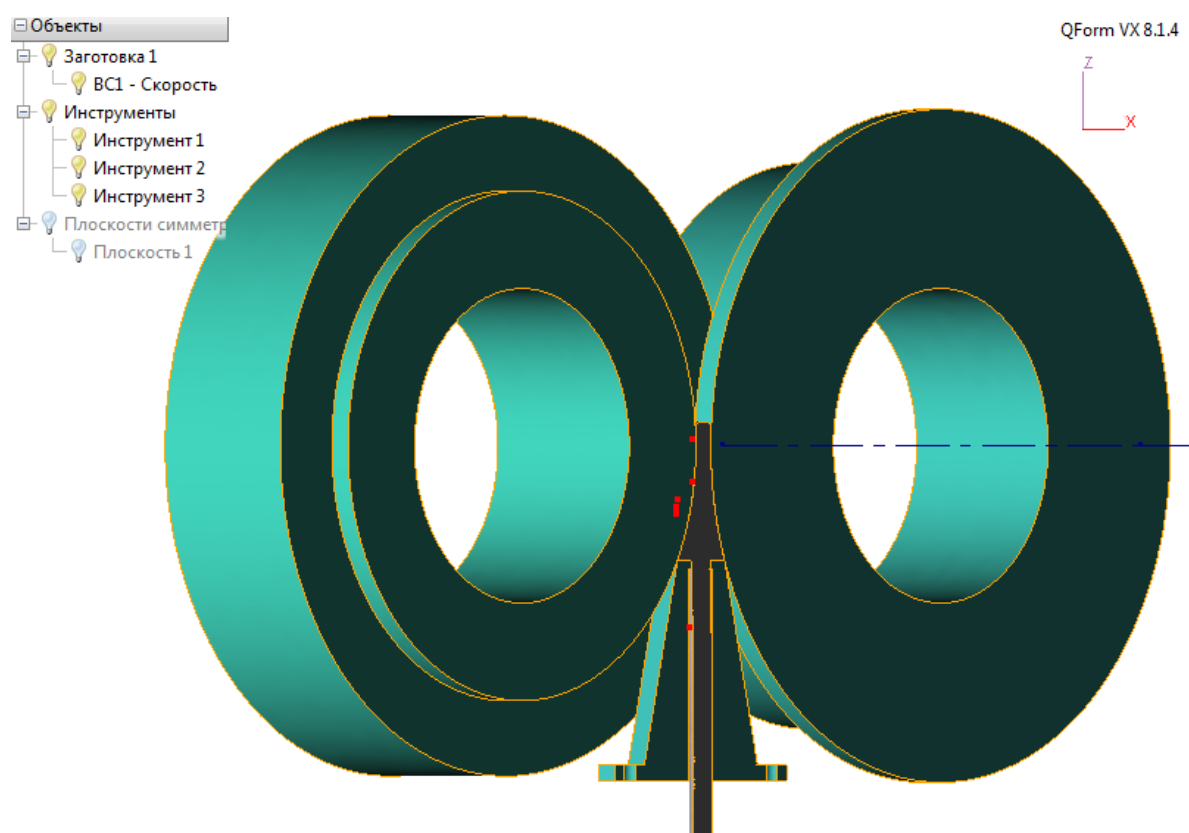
Схема процесса прокатки-прессования в отображении постановки задачи QFORM
